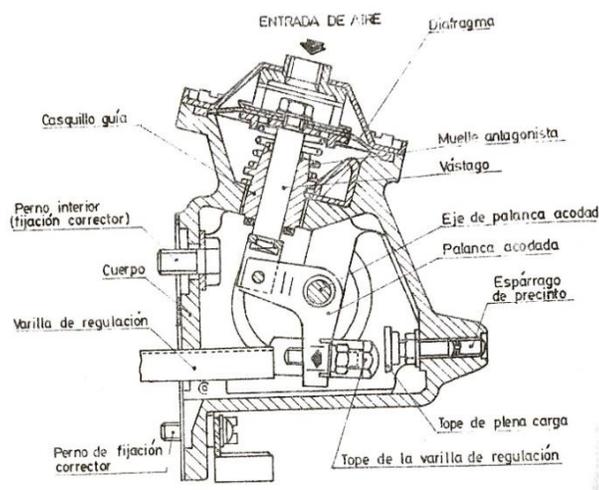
Partes principales de la bomba PE con volante y corrector de humos instalado sobre la parte anterior de la bomba
